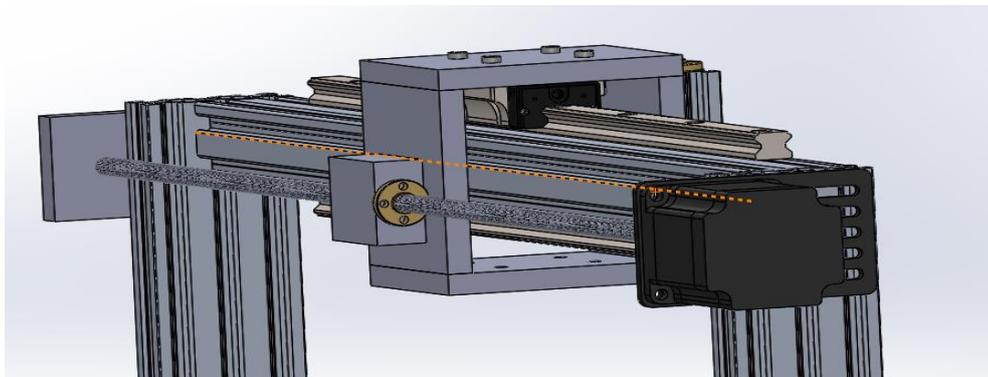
Assemblage complet de l'axe X de la machine CNC 5 axes.
